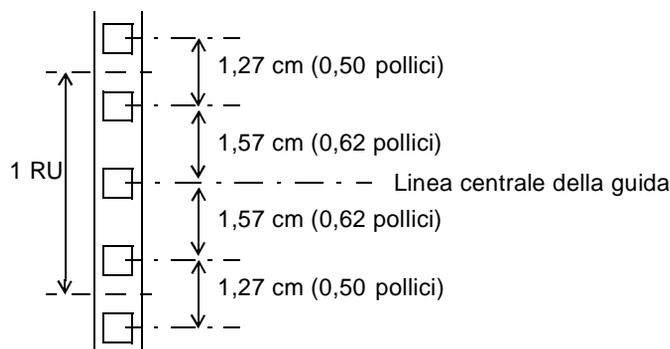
Dimensioni della spaziatura universale di fori EIA/RETMA per il montaggio
